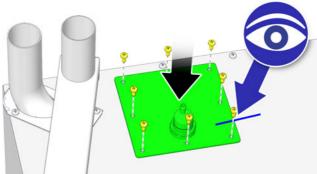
Tôle de montage du capteur de niveau de remplissage
